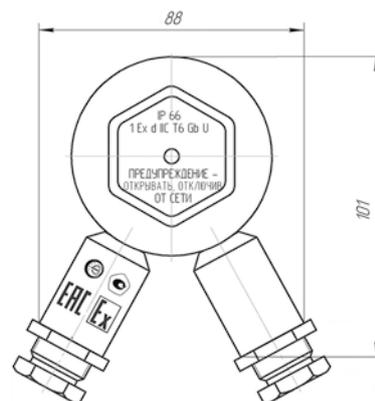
Габаритный чертеж головки соединительной с двумя кабельными вводами. Остальное см. рисунок 1
